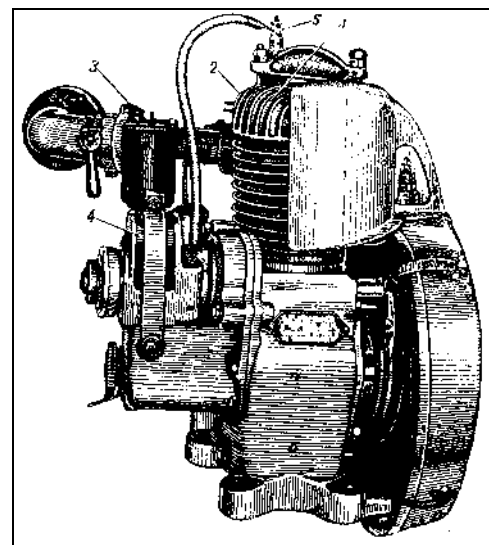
Двигатель типа В-3: 1 – цилиндр; 2 – ребра;
